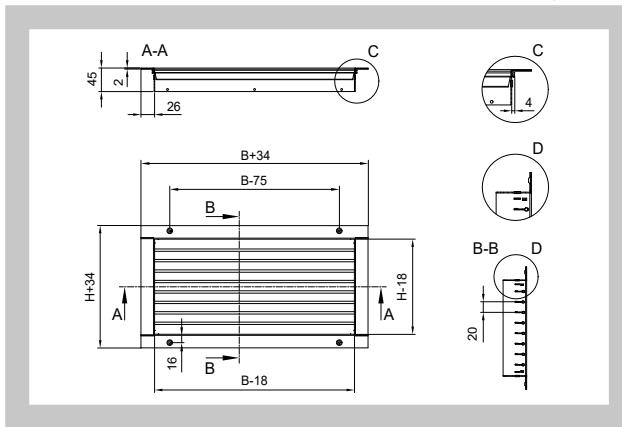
Einstellbare Lamellen horizontal - einreihig B > 750 mm
